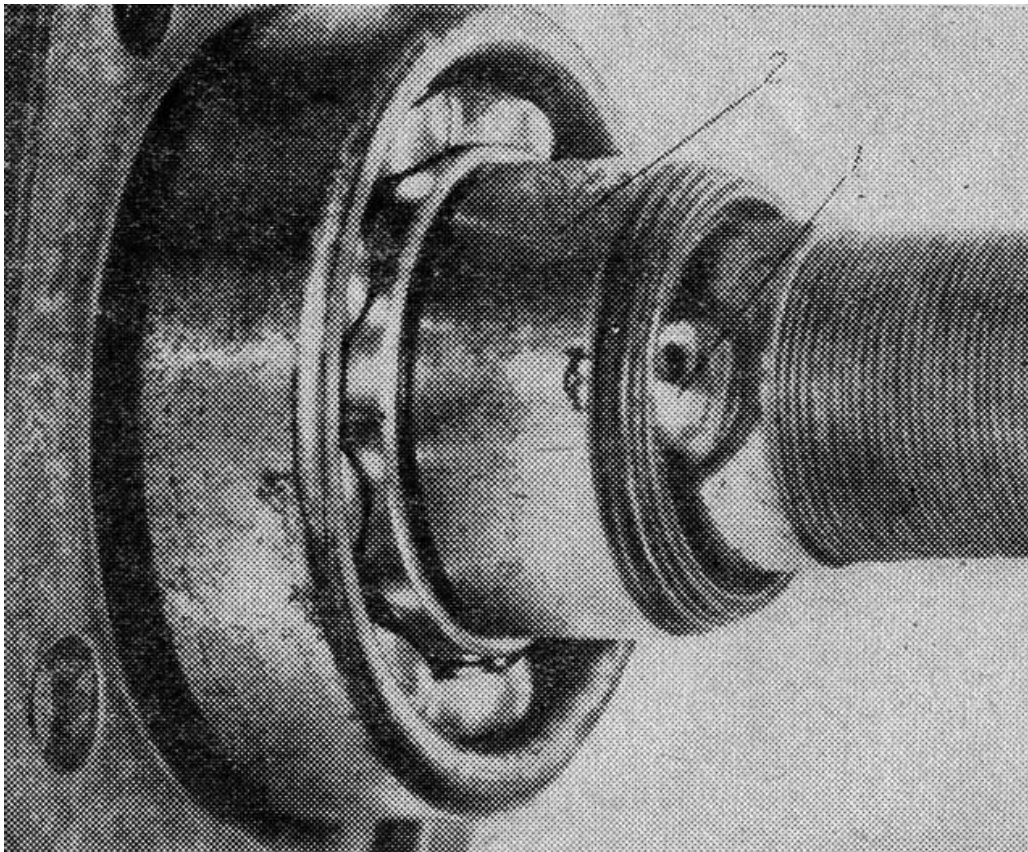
Дополнительное стопорение втулки подшипника полуоси:
